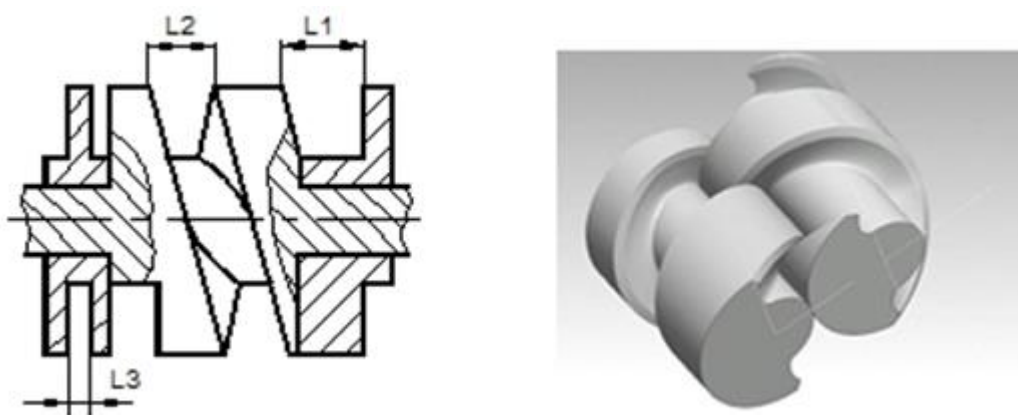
Сборный ротор компрессора и два ротора в сборе
